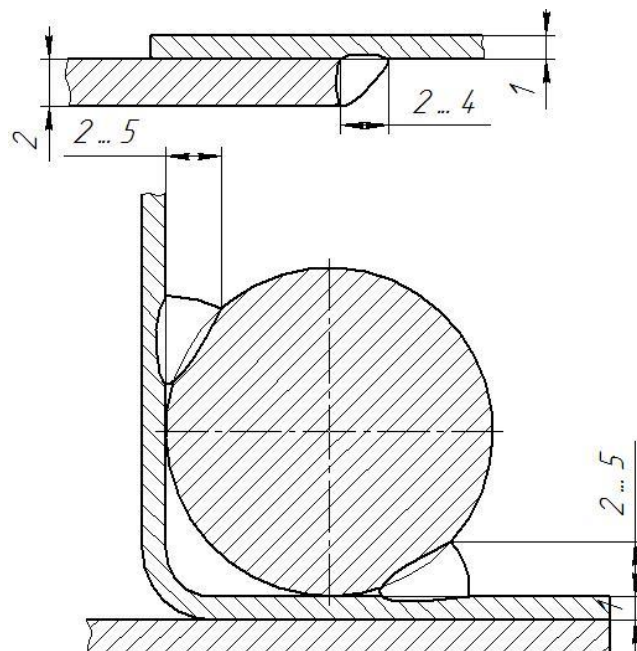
Размеры сварного соединения при выполнении сварных швов с применением дуговой сварки
